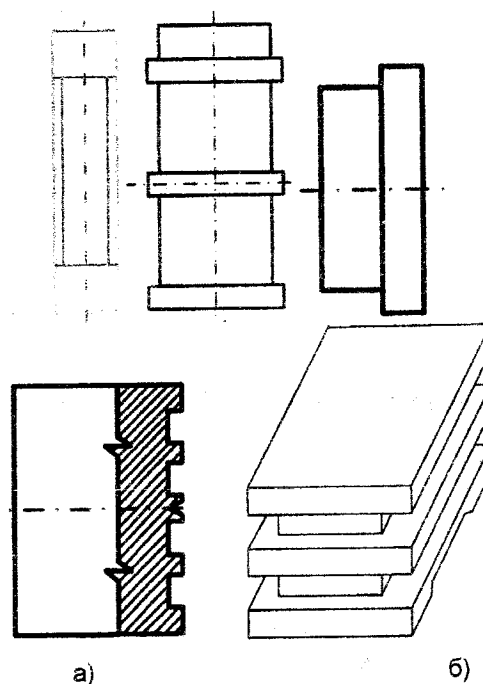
Образцы-изделия для проверки точности МРС: а – токарно-винторезных (ТВС); б – вертикально-фрезерных (ВФС)
